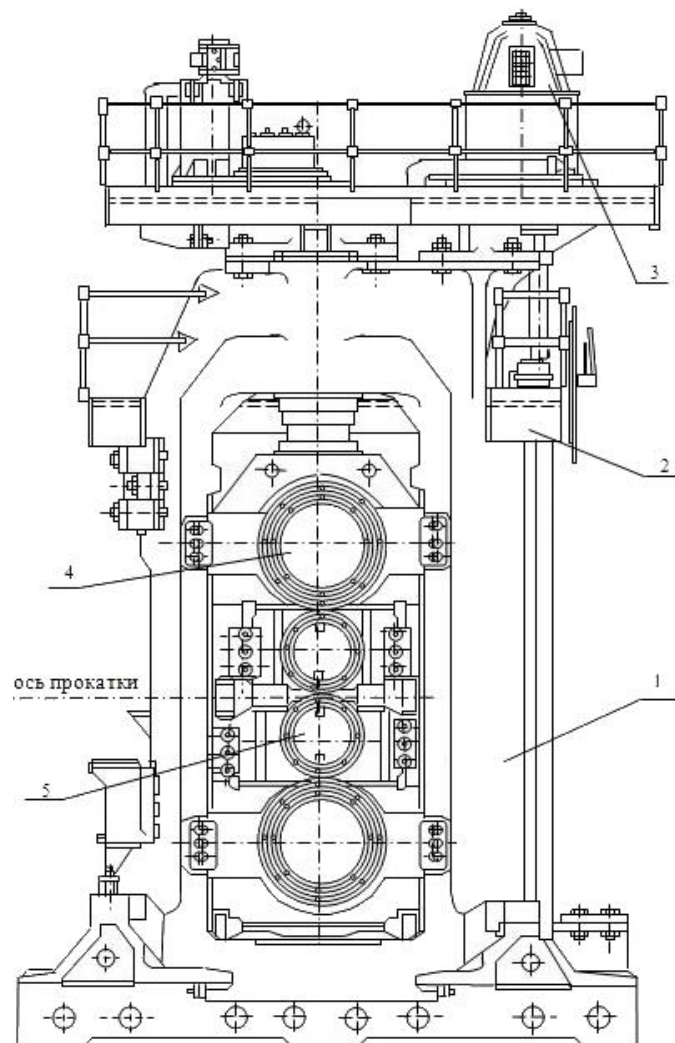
Чорнова кліть «кварто»: 1 – станина; 2 – шпинделі; 3 – електродвигун; 4 – валок опорний; 5 – валок робочий.
